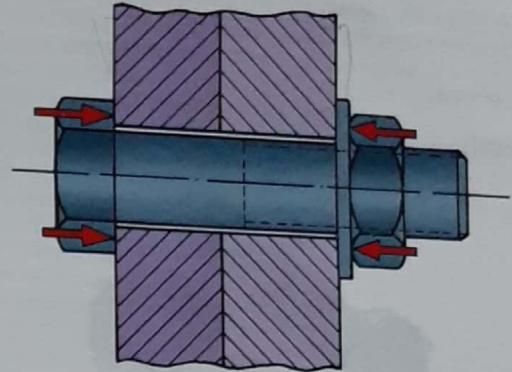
Ensamblaje atornillado mediante tornillo con cabeza y tuerca.
